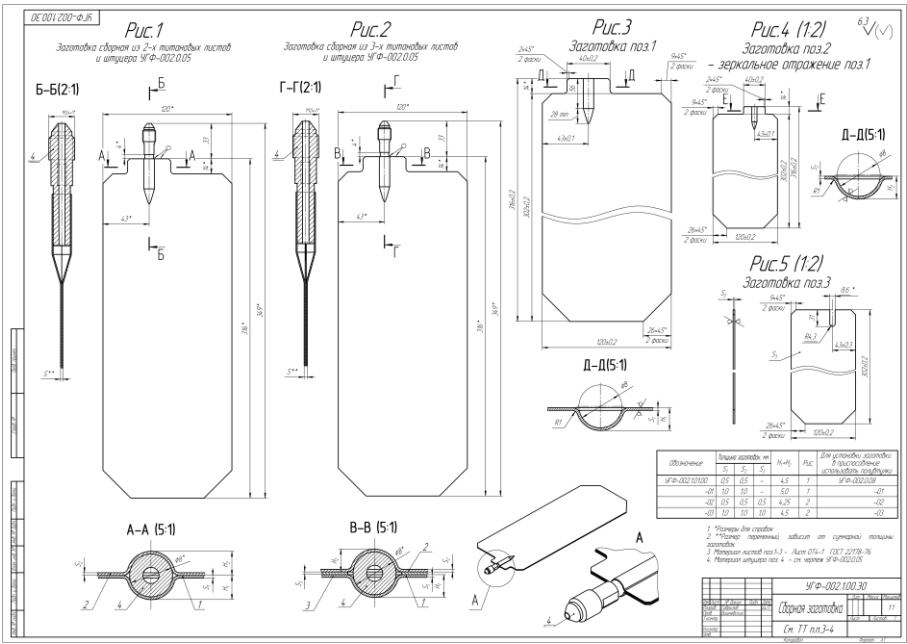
Заготовки для дослідження деформування елементів порожнистої лопатки
